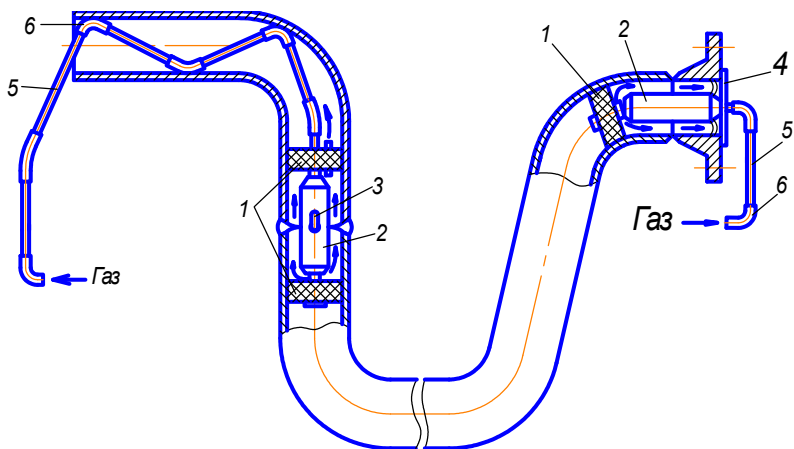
Схема применения защитных устройств для экономичного поддува: 1 – шайбы пенополиуретановые; 2 – ёмкость балластная; 3 – контакт сигнального устройства; 4 – заглушка металлическая; 5 – трубка металлическая; 6 – трубка резиновая
